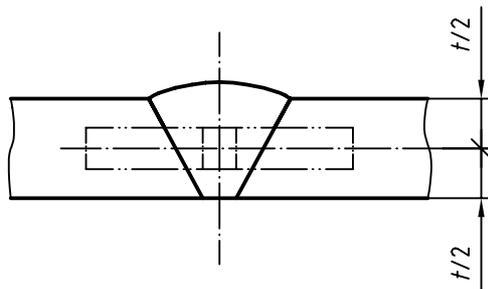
Position de l'éprouvette entaillée d'essai de flexion par choc dans la pièce d'essai
